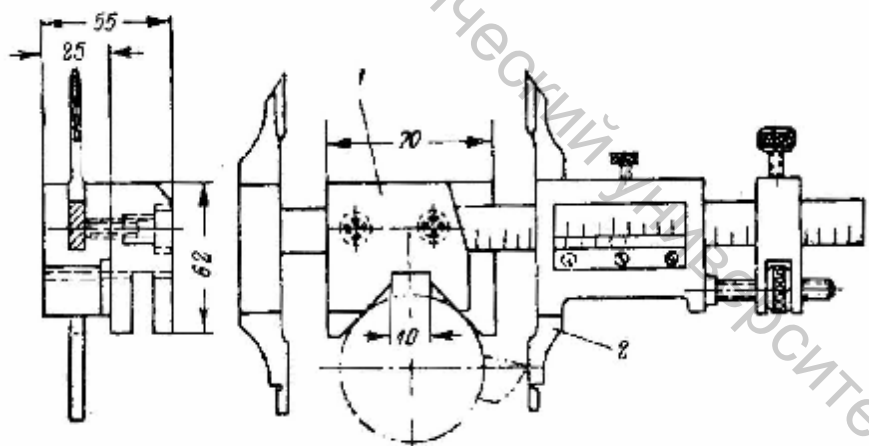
Штангенциркуль со шкалой для установки резцов
